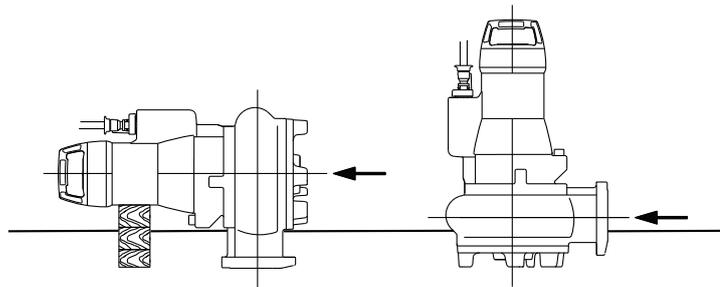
Schmierflüssigkeitsstand prüfen a) Ausführung YL & WL; b) Ausführung YL & WL bei Baugröße 50-170, 50-172 und 65-220
